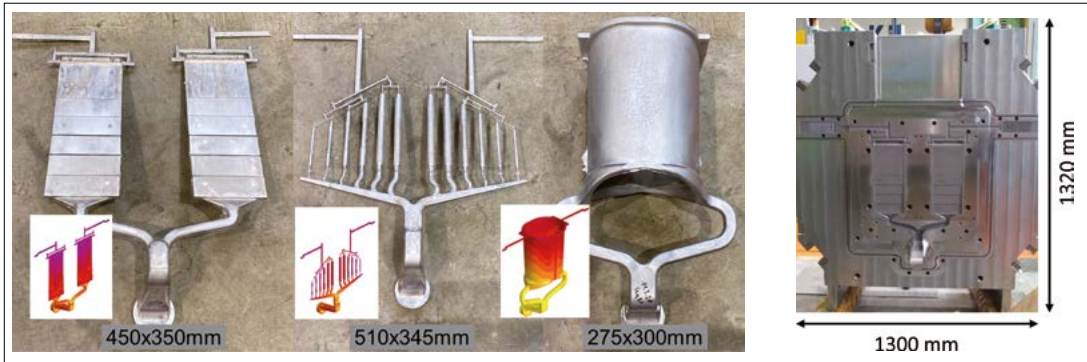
Derzeit bestehende Geometrien: Doppelstufenplatte, Rundzugproben und Gussrohr (links), Gesamtansicht des modularen Werkzeuges mit Doppelstufenplatte (rechts)
